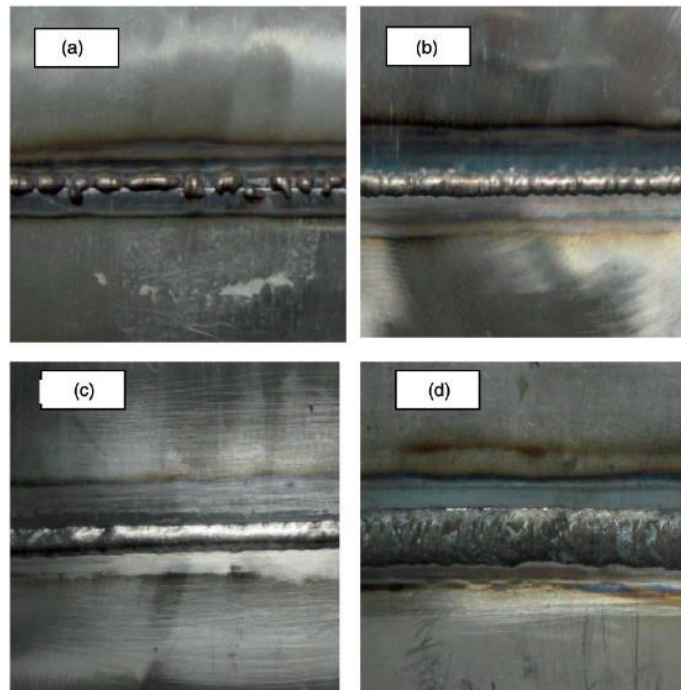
Configuración de soldadura en a) Fusión incompleta, b) Ausencia de penetración, c) Buena soldadura, d) Exceso de penetración [14]
